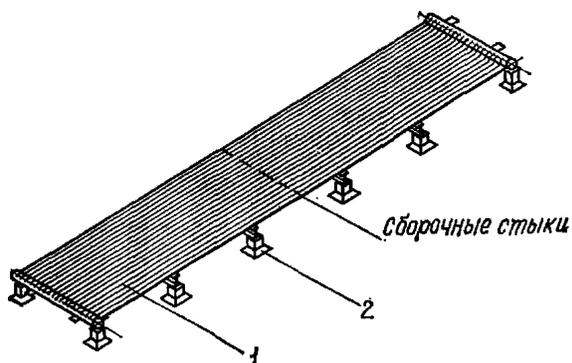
Укрупнение блока поверхности нагрева на сборочном приспособлении
